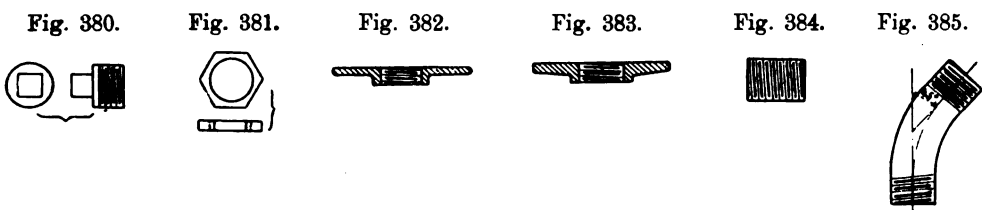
die Gegenmutter (zum Verdichten), Fig. 382 und 383 die Flanschen, Fig. 384 das sogenannte Langgewinde.
